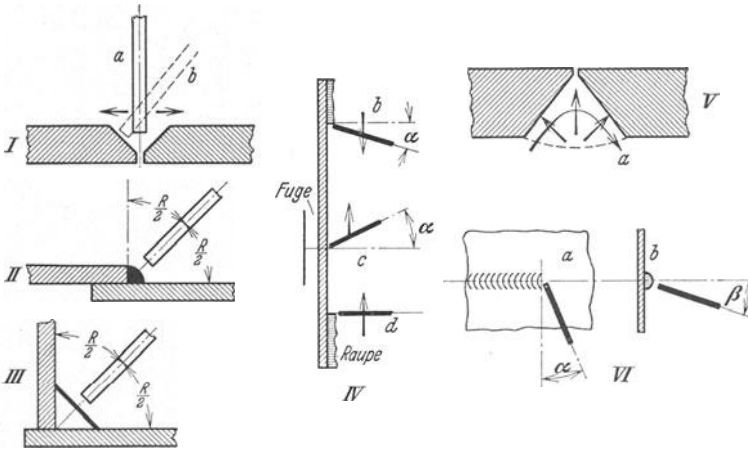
Elektrodenhaltung beim Schweißen in verschiedenen Stellungen.
